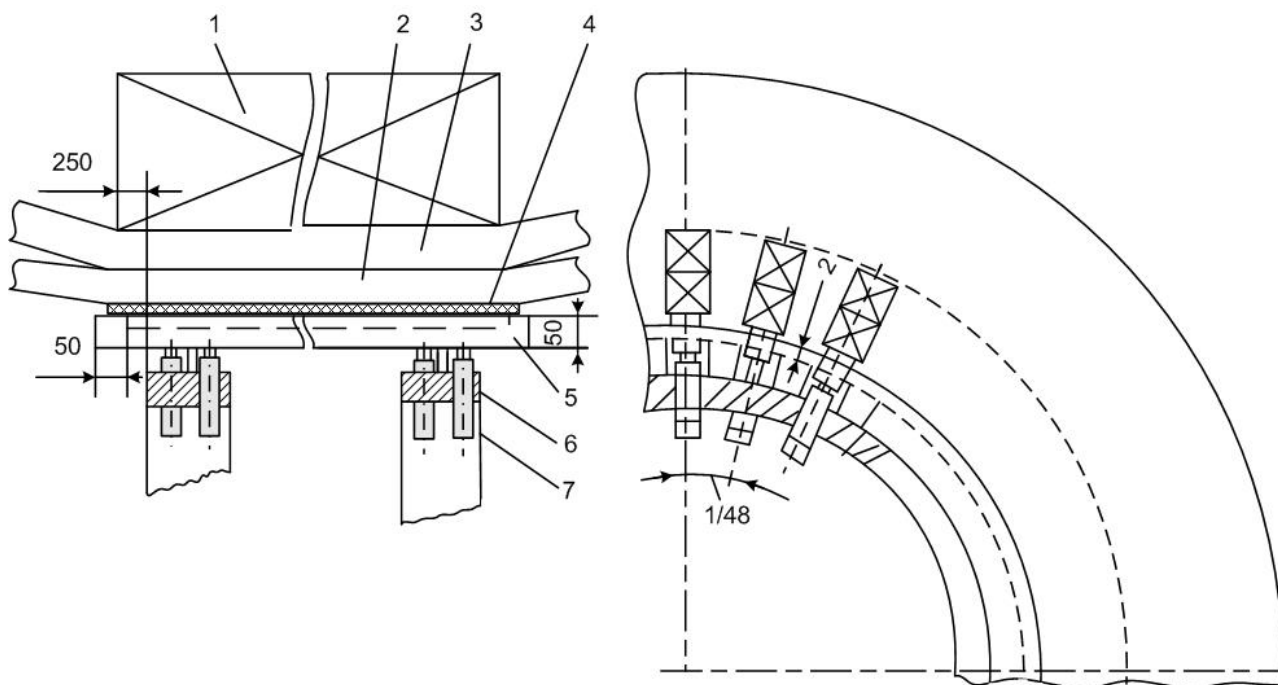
Опресовування пазової частини обмотки статора
